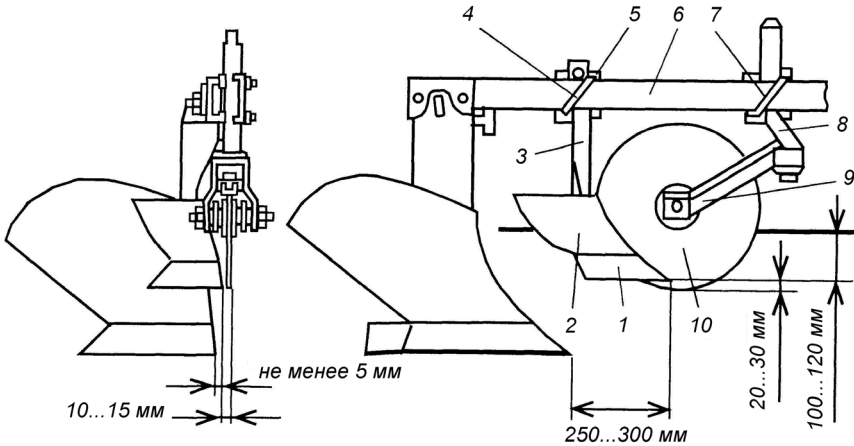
Схема установки рабочих органов плуга: 1 – лемех; 2 – отвал; 3 – стойка; 4, 7 – скобы; 5 – державка; 6 – грядиль; 8 – коленчатая стойка; 9 – вилка; 10 – дисковый нож
